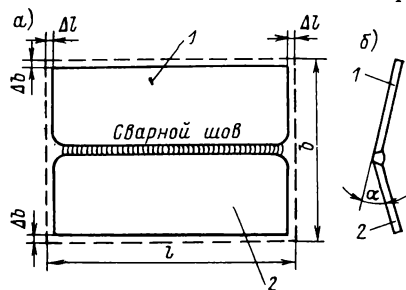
Схема возникновения сварочных деформаций: а — продольная усадка; б — угловая деформация. 1, 2 — сваренные детали; l — длина деталей; b — ширина деталей; Δl — усадка по длине; Δb — усадка по ширине; α — угол поворота при деформации.
